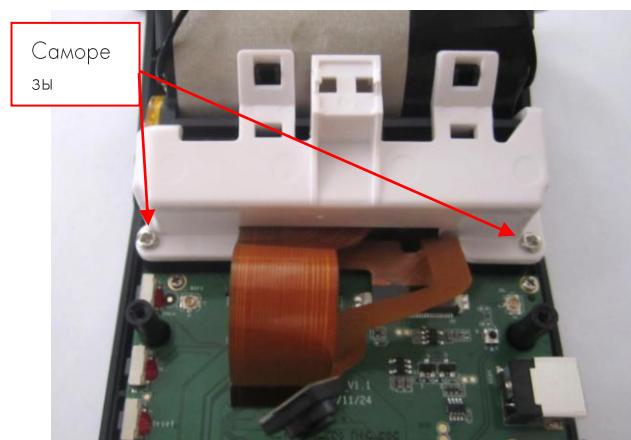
Саморезы, фиксирующие основание принтера и корпус верхний.
